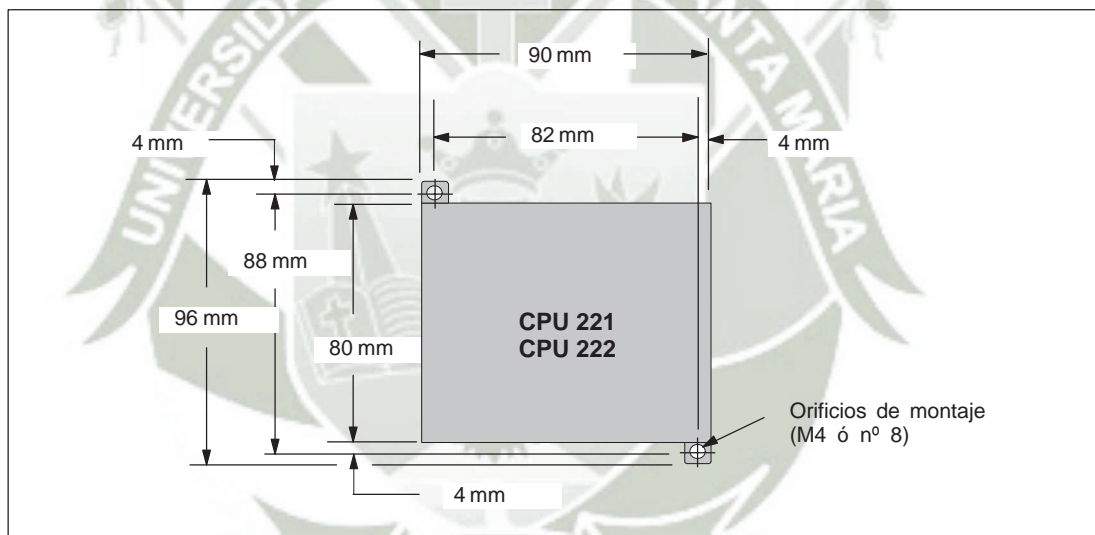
Dimensiones de montaje para una CPU 221 y una CPU 222
